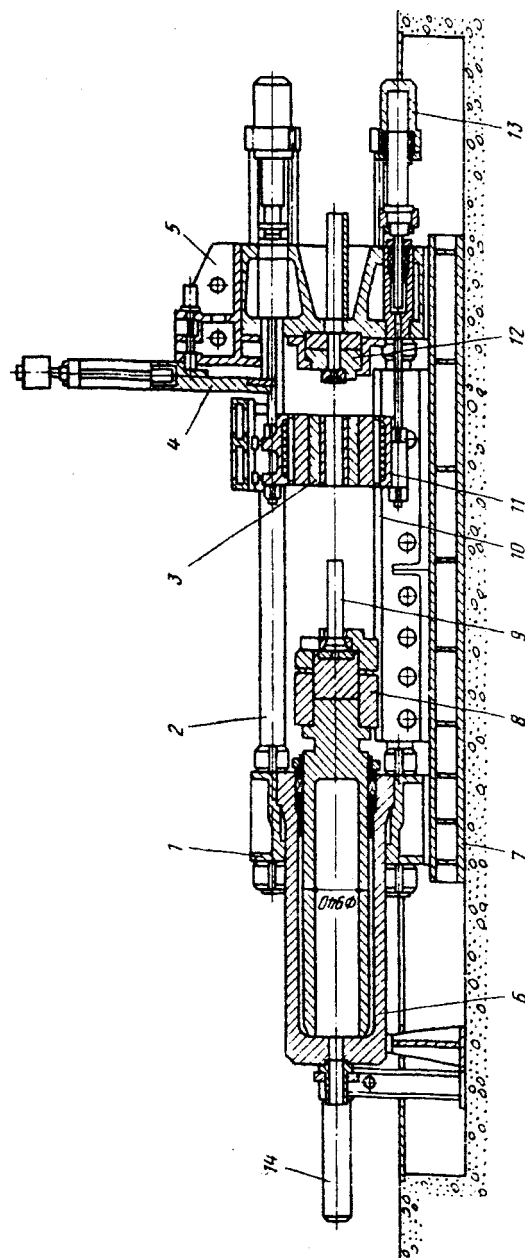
Прутково-профильный горизонтальный гидравлический пресс усилием 25 МН: 1 - задняя поперечина; 2 - колонна; 3 - контейнер; 4 - ножницы для отделения пресс-остатка; 5 - передняя поперечина; 6 - рабочий цилиндр; 7 - фундаментная плита, 8 - прессующая траверса; 9 - пресс-штемпель; 10 - призматические направляющие; 11 - контейнеродержатель, 12 - матрицедержатель; 13 - цилиндры передвижения контейнера; 14 - форсирующий цилиндр
